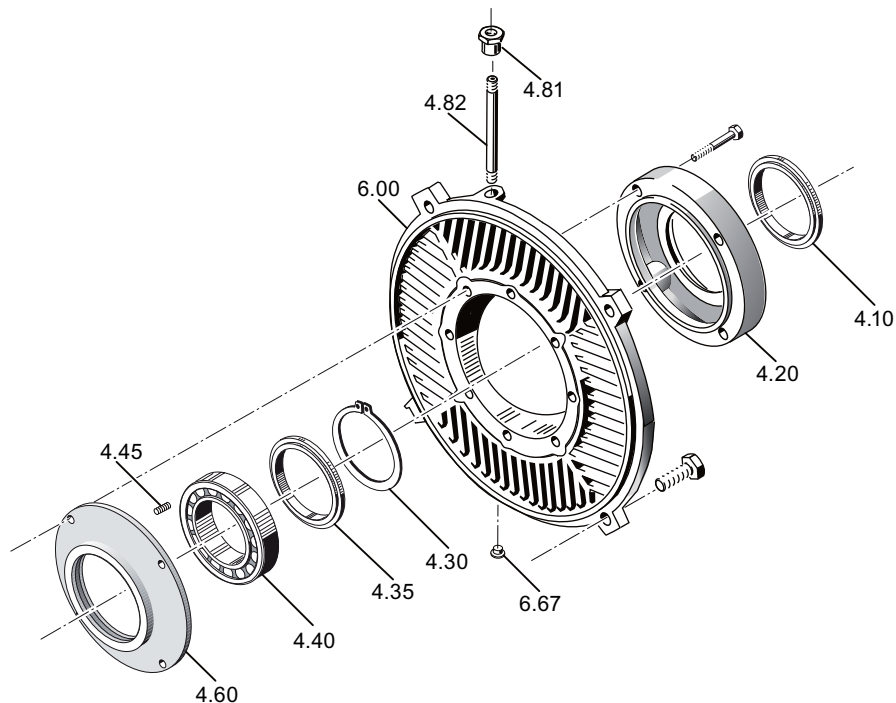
Подшипник качения, неприводная сторона (NDE) без корпуса подшипника
